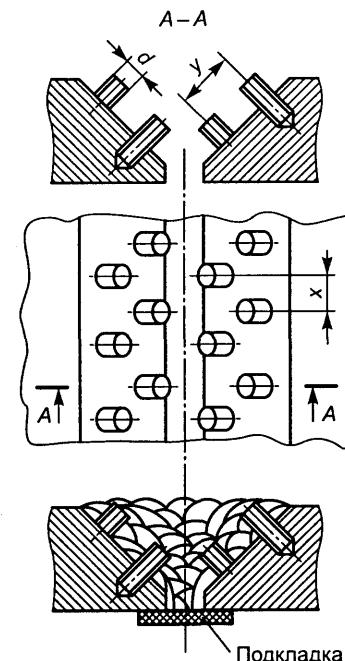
Схема расположения шпилек и заварка места разделки:
